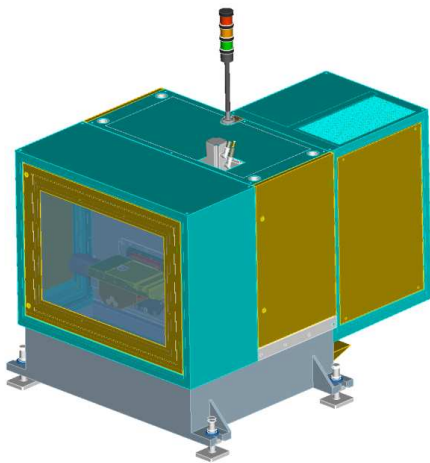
Schéma CNC systému s rotačním motorem a kuličkovým šroubem
